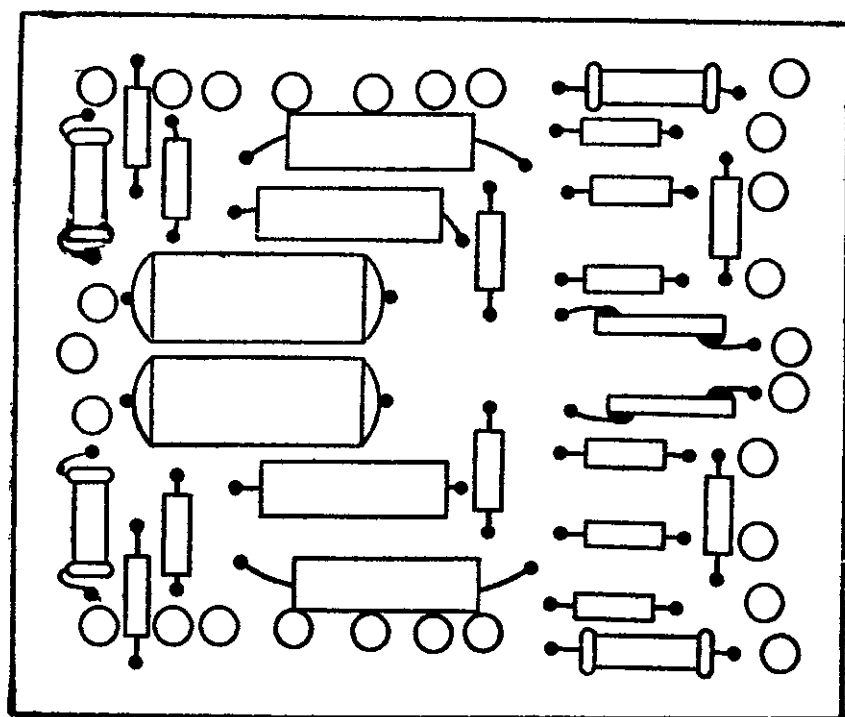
Печатная плата усилителя со стороны расположения деталей
